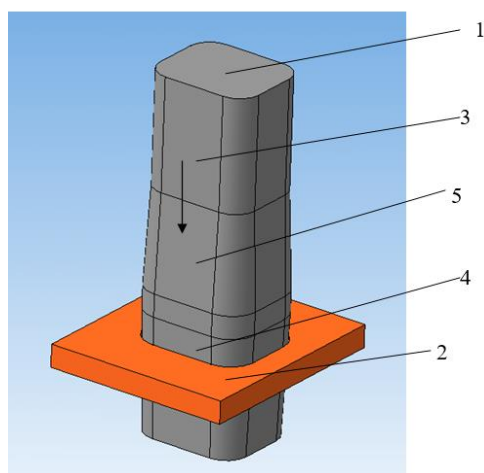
Схема процесу дорнування профільного отвору: 1 - профільний інструмент; 2 – заготовка; 3 – хвостовик; 4 - робоча конусна частина; 5 - конусна хвостова частина
